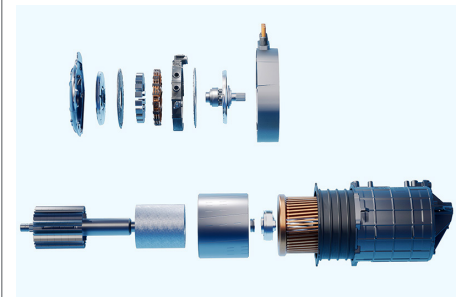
Comparaison des composants. En dessus se trouve la petite et légère machine à flux axial, en dessous se trouve la machine à flux radial.
